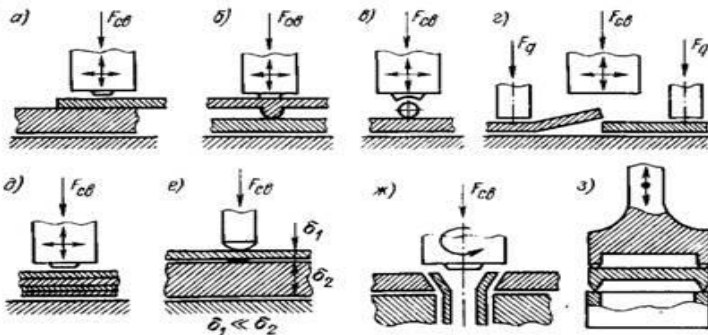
Основные типы сварных соединений металлов при УЗС [6]: а – внахлест; б – по профилю; в – параллельное соединение круглого и плоского профилей; г – с деформированием кромок; д – многослойных элементов; е – детали разной толщины; ж – угловое соединение; з – контурная сварка элементов. Стрелками показано направление колебаний сварочного наконечника.
